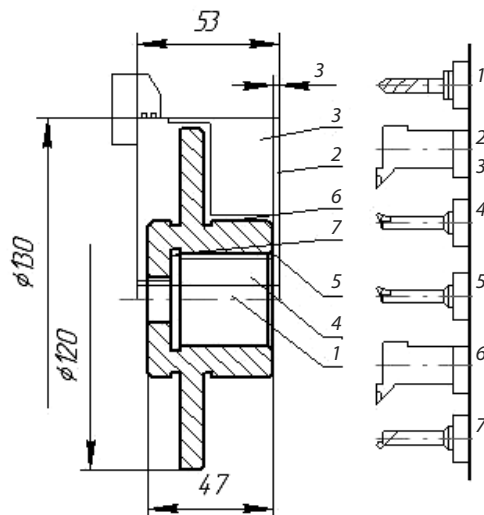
Типовая последовательность обработки с назначенной совокупностью режущих инструментов:
